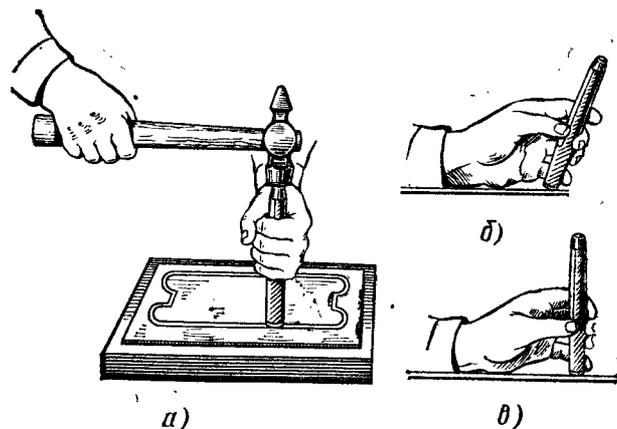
Вырубание заготовок навесным ударом и установка зубила:
